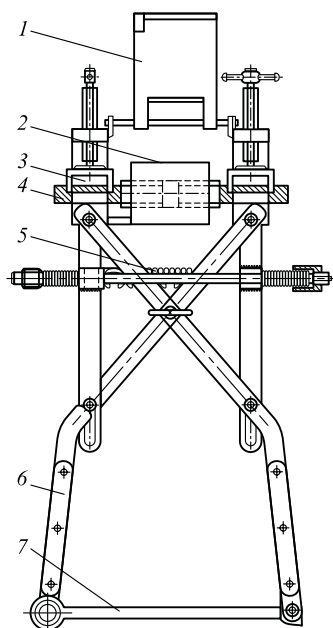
Клещи для термитной сварки проводов:
